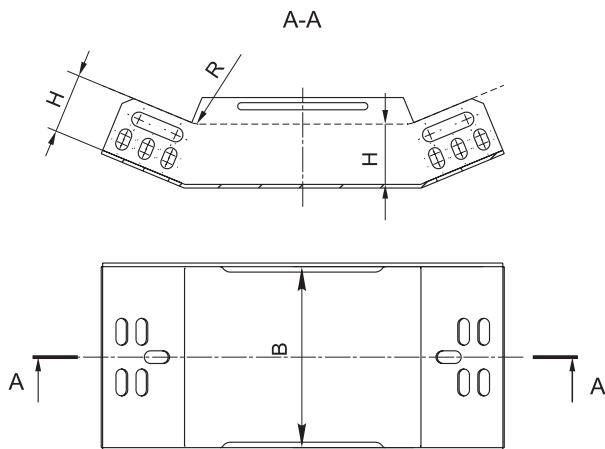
Поворот 45° вертикальный внутренний. Размеры для размещения кабеля / Figure C.1 – 45° vertical internal bend. Dimensions for cable placement
